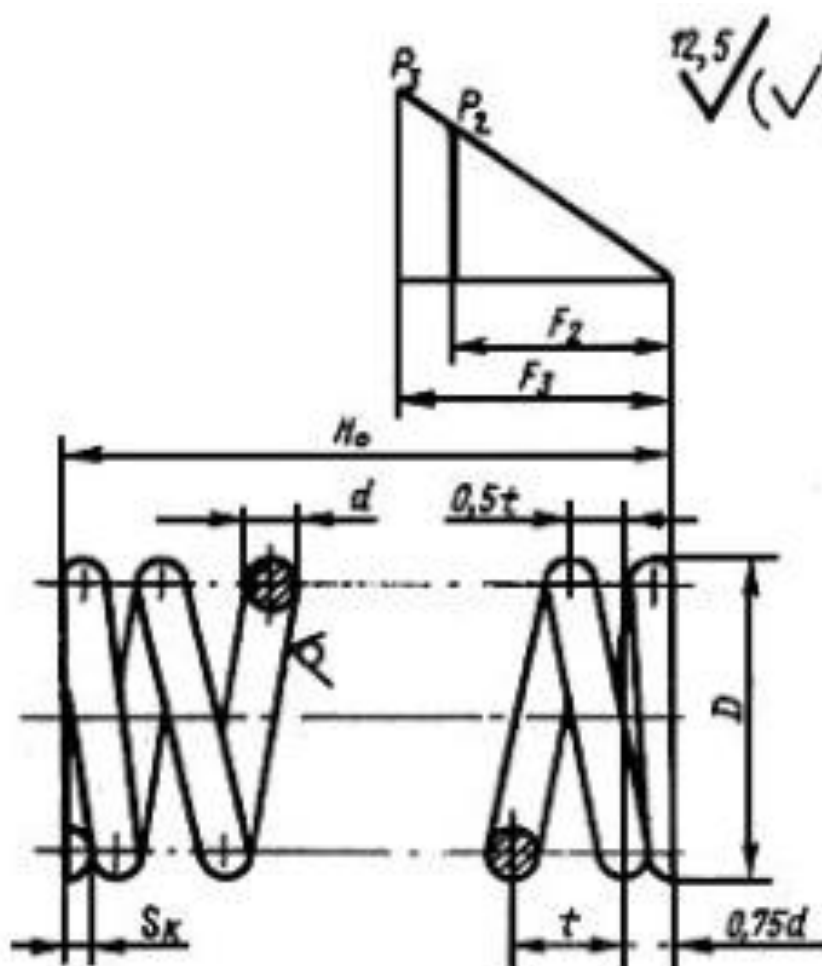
Чертеж винтовой цилиндрической пружины сжатия
